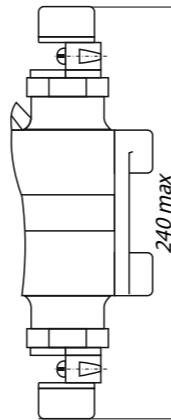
Светильник со штуцерами под открыто проложенный кабель остальное см. Рис. 1
